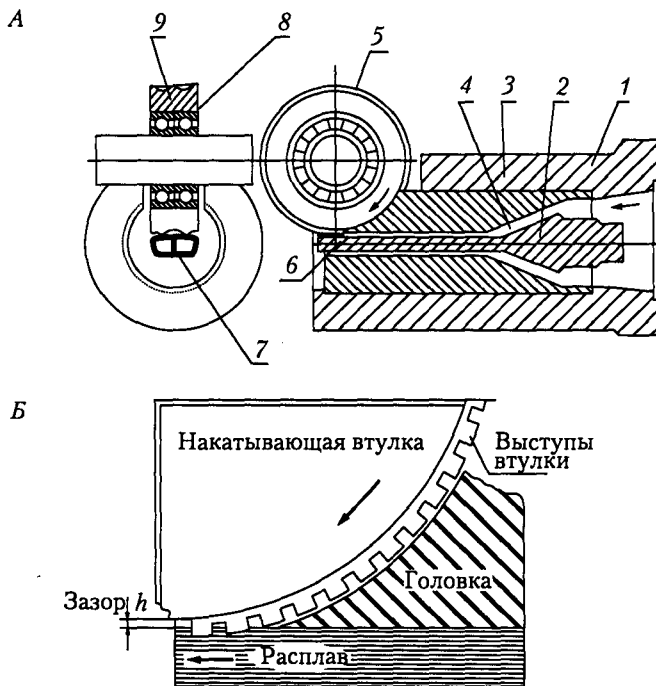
Технологическая схема изготовления рельефных профилей: А — общая схема работы; Б — схема работы накатывающей втулки
